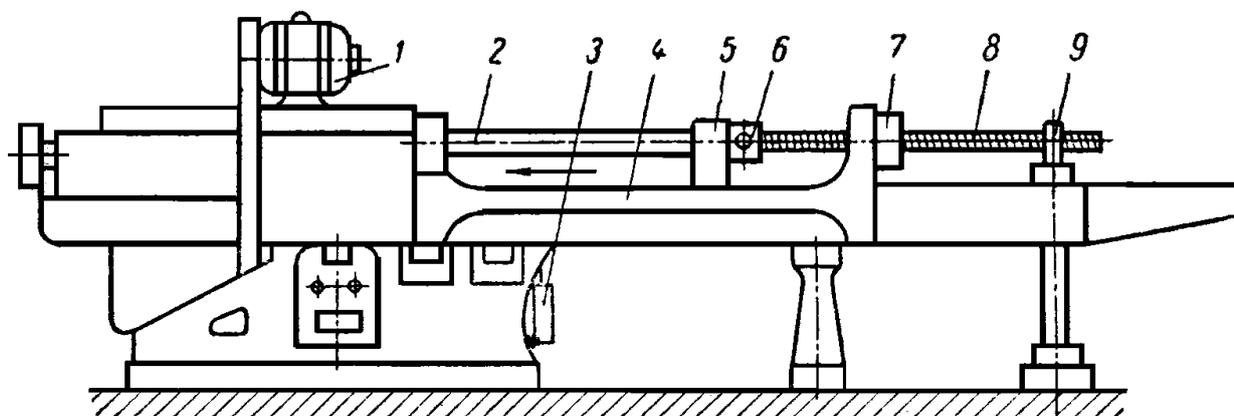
Общий вид горизонтально-протяжного станка: 1 – электродвигатель; 2 – шток; 3 – гидропривод; 4 – станина; 5 – ползун; 6 – зажимное приспособление; 7 – заготовка; 8 – протяжка; 9 – люнет
